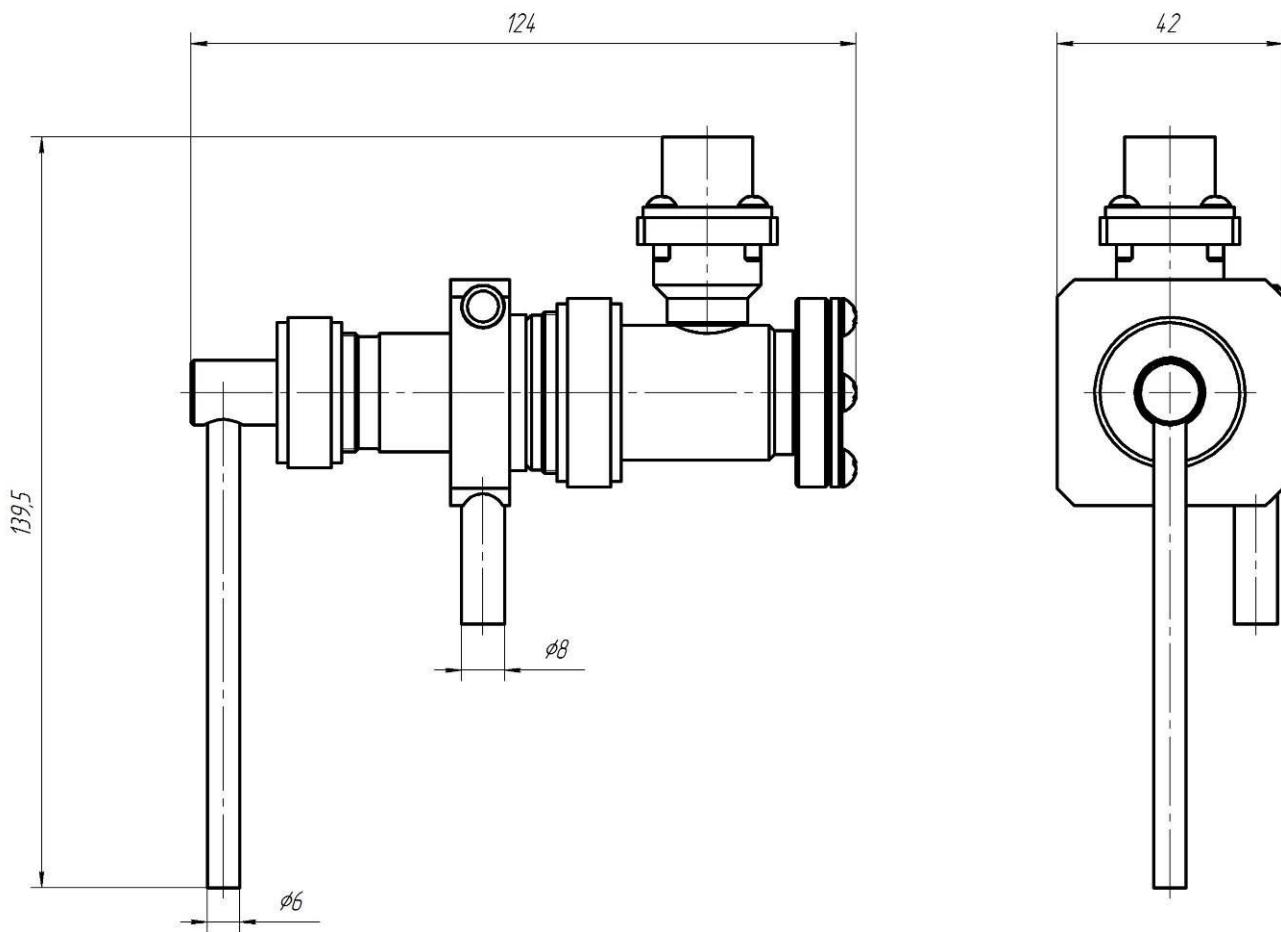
Габаритный чертеж проточного блока датчиков ДК-7.
